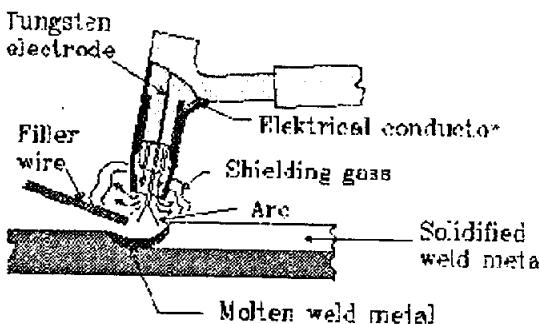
Tig - Welding - Hàn Tig
